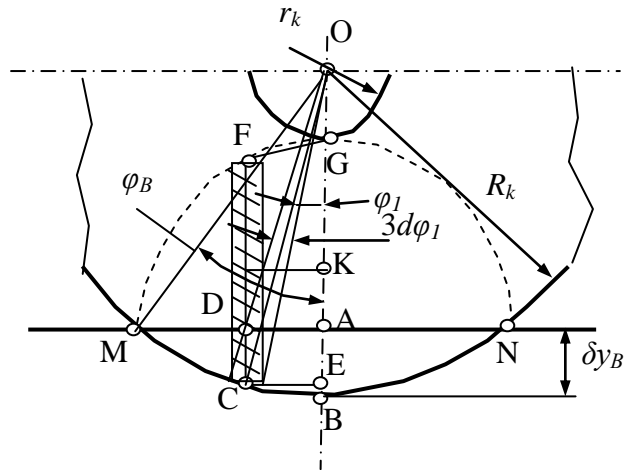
Схема к расчету площади деформированного материала круга
